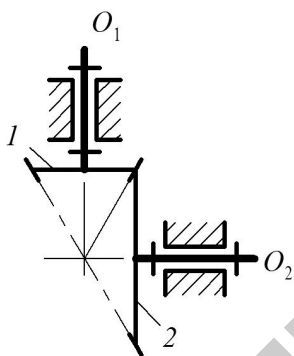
Схема зубчатой передачи с коническими колесами
